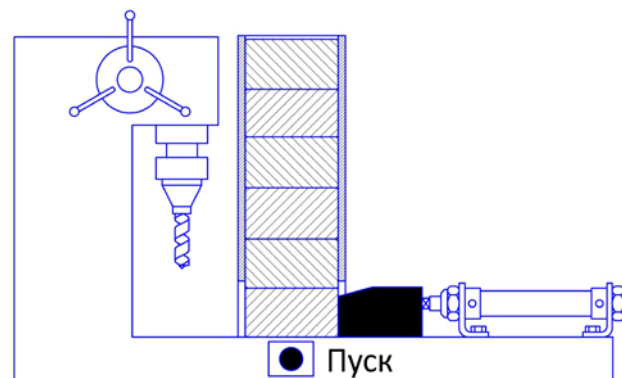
Сверлильный станок с механизированной подачей заготовок на рабочую позицию.
